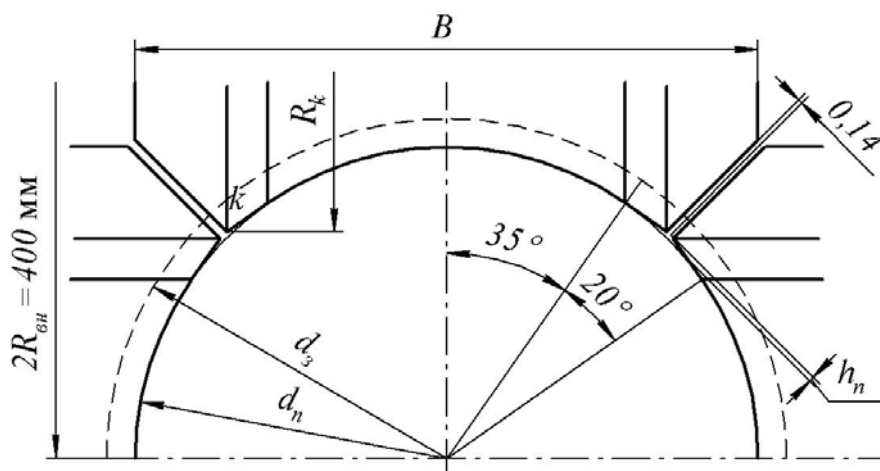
Схема калибровки «круг-круг» с подрезанием фасок
